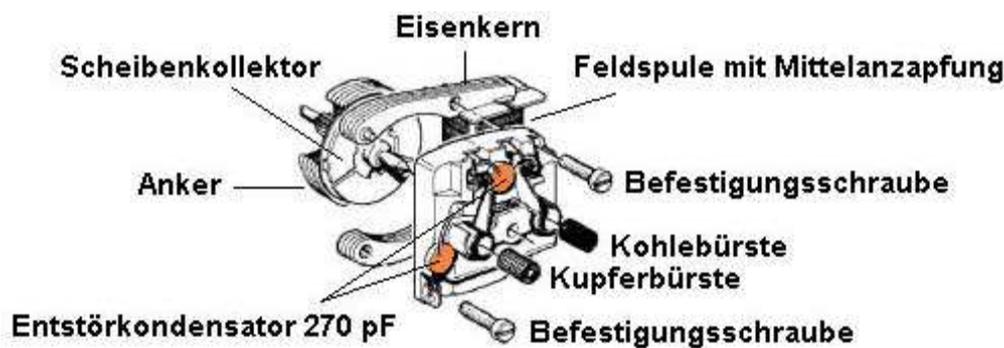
Mechanischer Aufbau eines großen Scheibenkollektormotors (LFCM) mit Feldspule (Allstrommotor)
